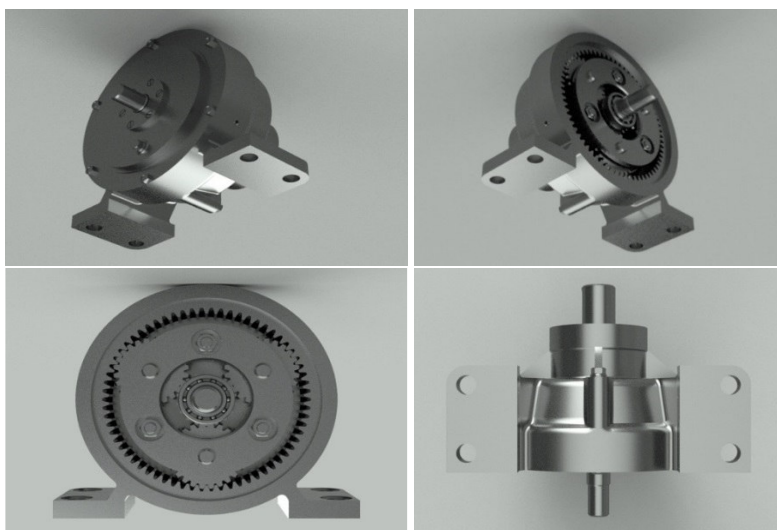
3D модель одноступенчатого планетарного редуктора
